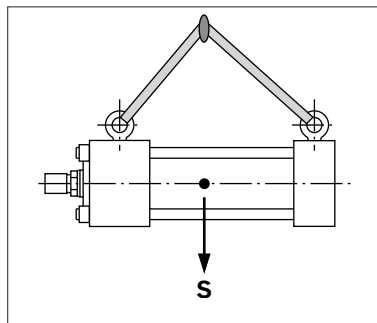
Transport mit Ringschrauben und Hebegeräten [1. a)]
